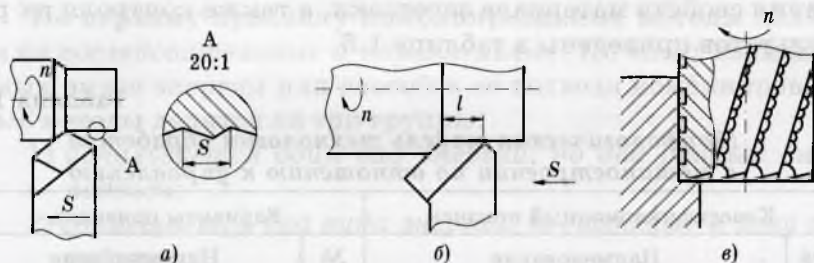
Схема изменения длины контакта режущей кромки с направляющей и образующей
